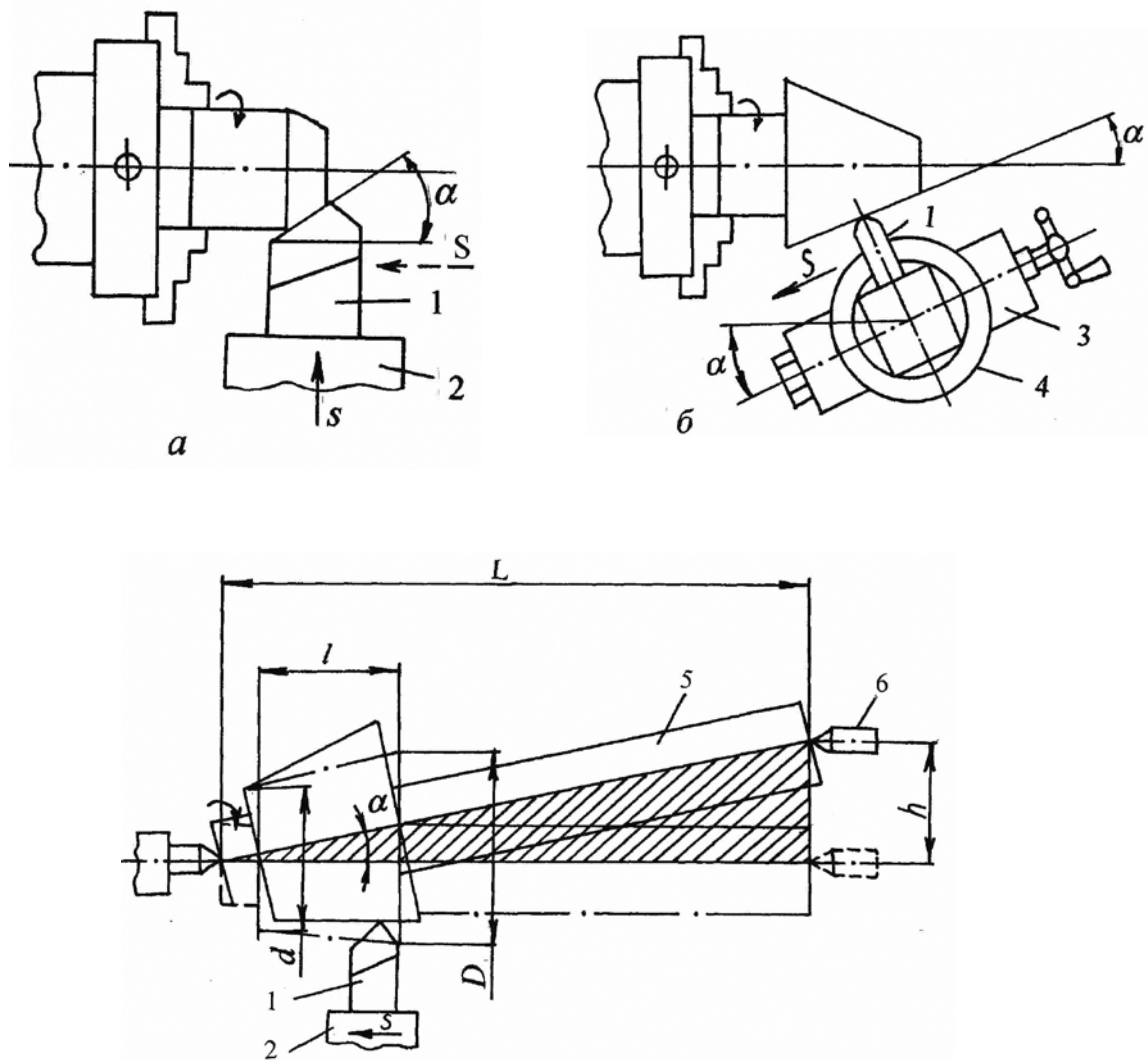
Схемы обработки конических поверхностей на токарно-винторезных станках: *а* – широким резцом; *б* – поворотом резцовых салазок; *в* – смещением корпуса задней бабки
